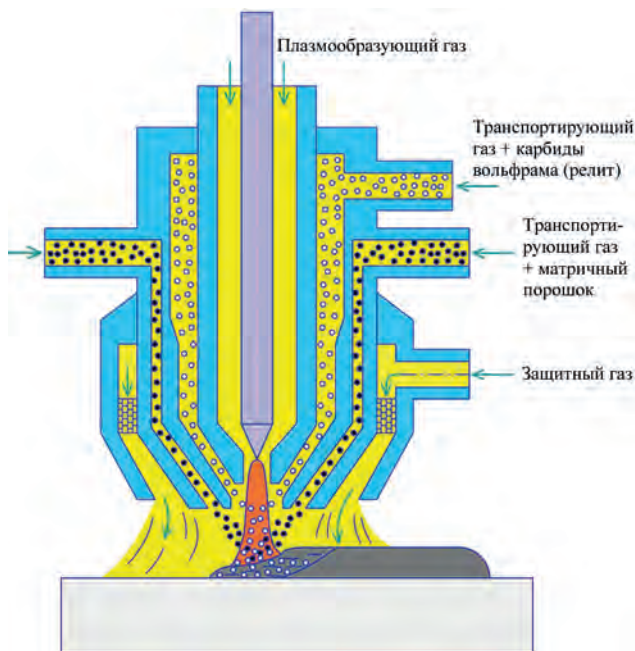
Схемы плазменно-порошковой наплавки с подачей релита в сварочную ванну через осевое отверстие фокусирующего сопла
